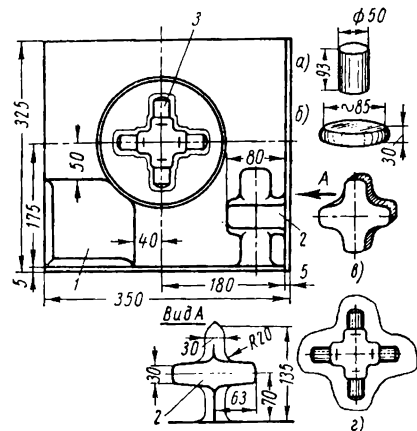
Переходы штамповки для крестовины и штамп с формовочным ручьем: а — исходная заготовка; б — заготовка после осадки; в — заготовка после формовочного ручья; г — отштампованная поковка с заусенцем; 1 — площадка для осадки; 2 — формовочный ручей; 3 — окончательный ручей
